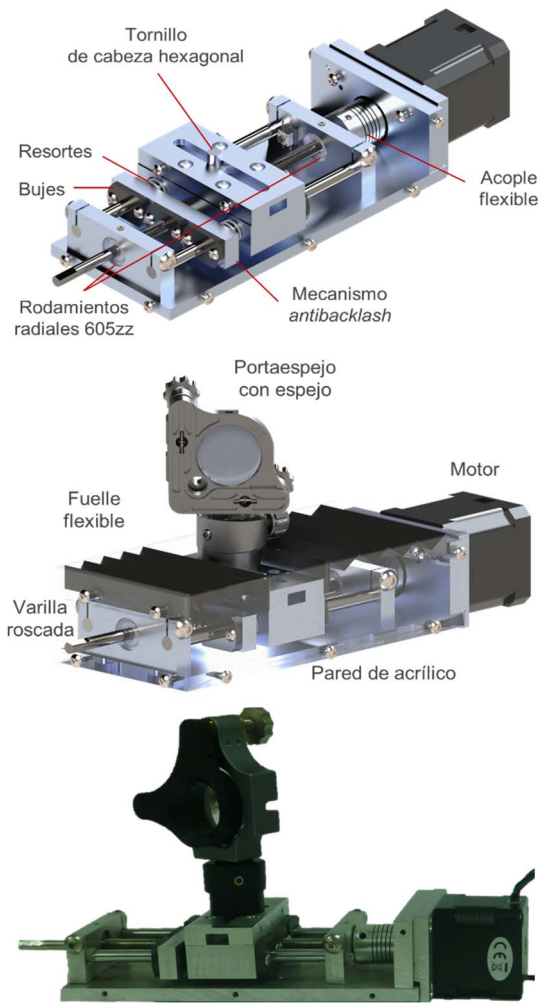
Dispositivo desarrollado para desplazar el espejo. Arriba: diseño CAD de los componentes internos. Centro: diseño CAD de la vista externa. Abajo: fotografía del dispositivo fabricado con vista de los componentes internos.
